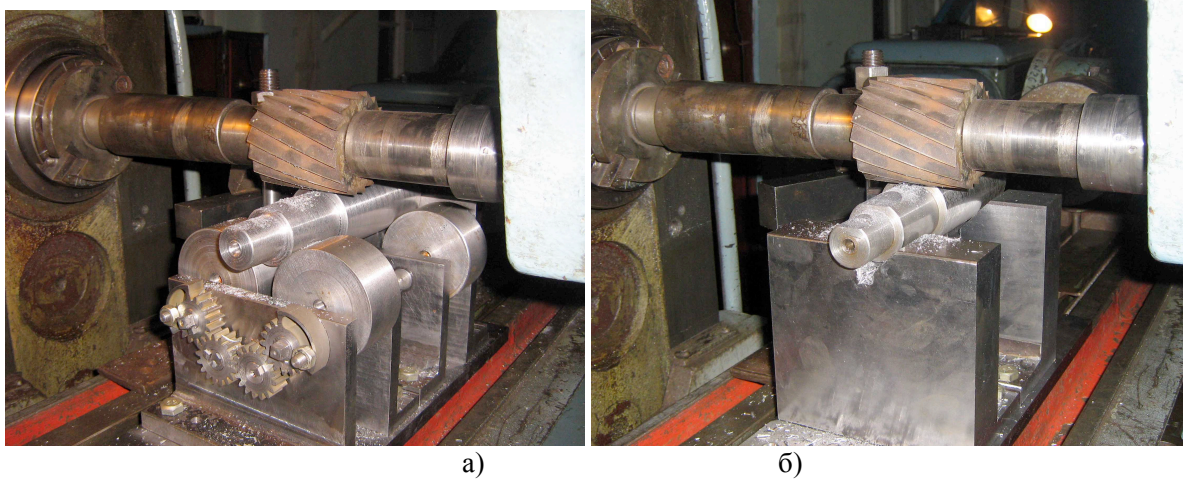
Фрезерування лиски на горизонтально-фрезерному верстаті мод. 6Р82Г при установці заготовок: а – на запропоновану базуючу призму; б – на жорстку опорну призму
